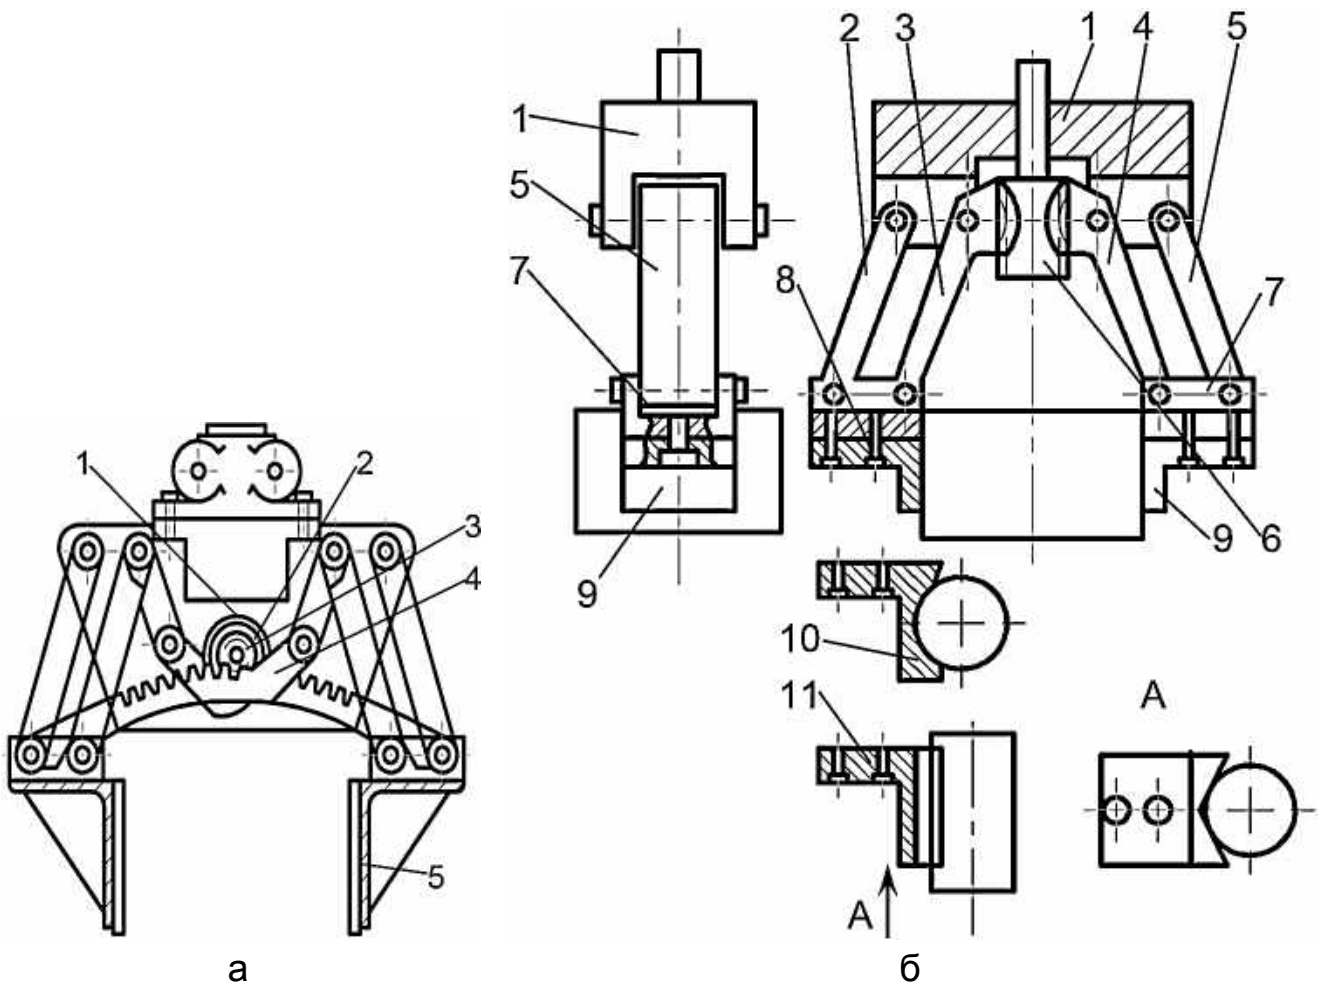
Центрувальні широкодіапазонні захоплювальні пристрої
